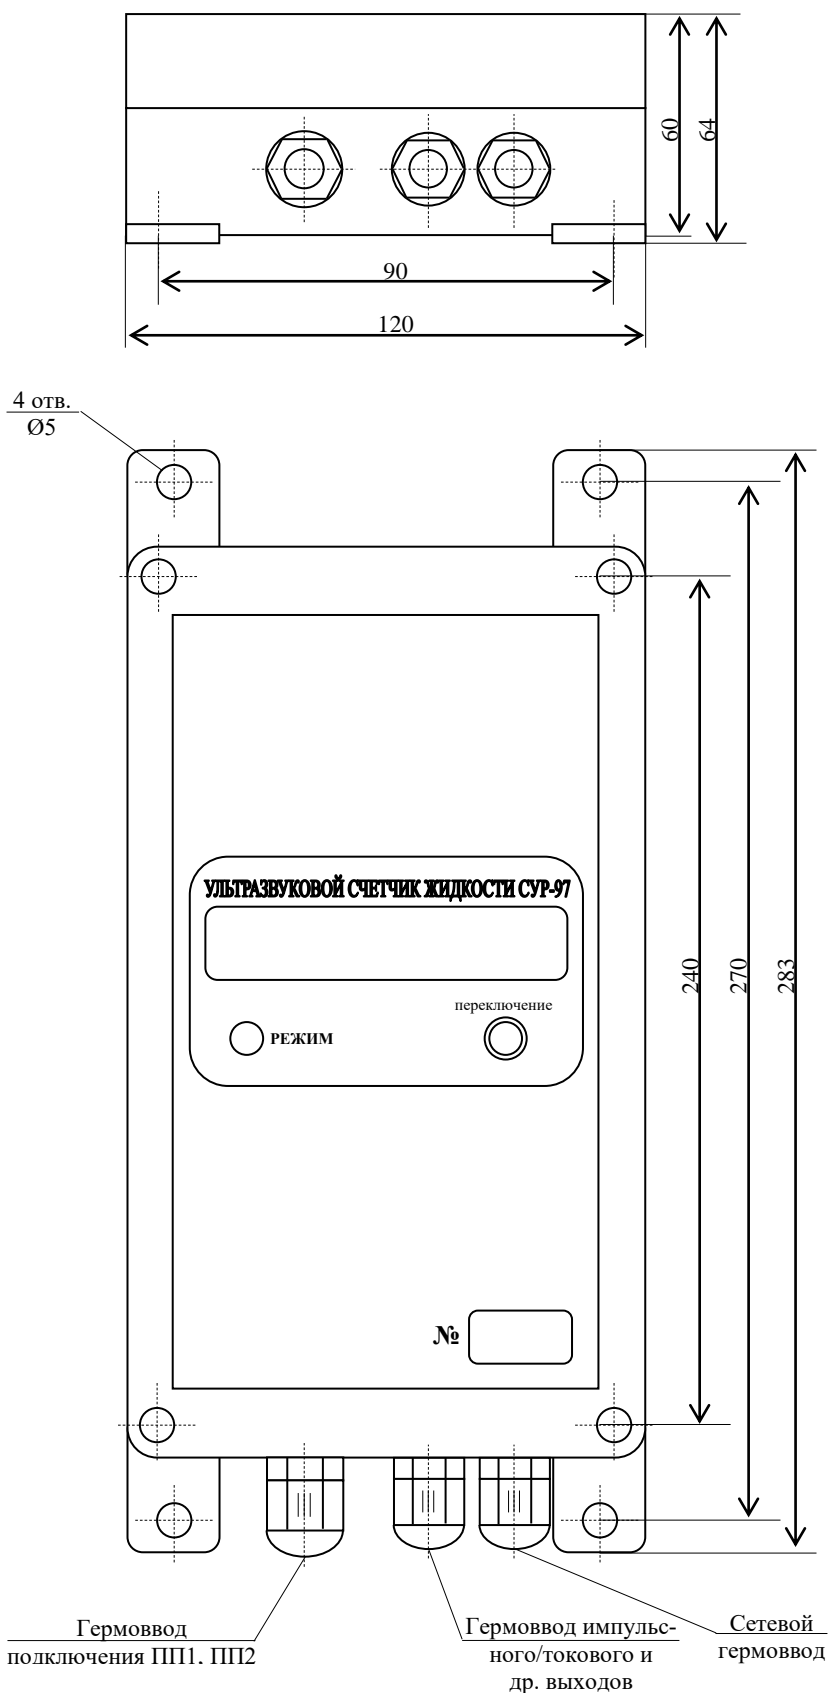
а - Внешний вид ЭП (габариты, установочные размеры)
